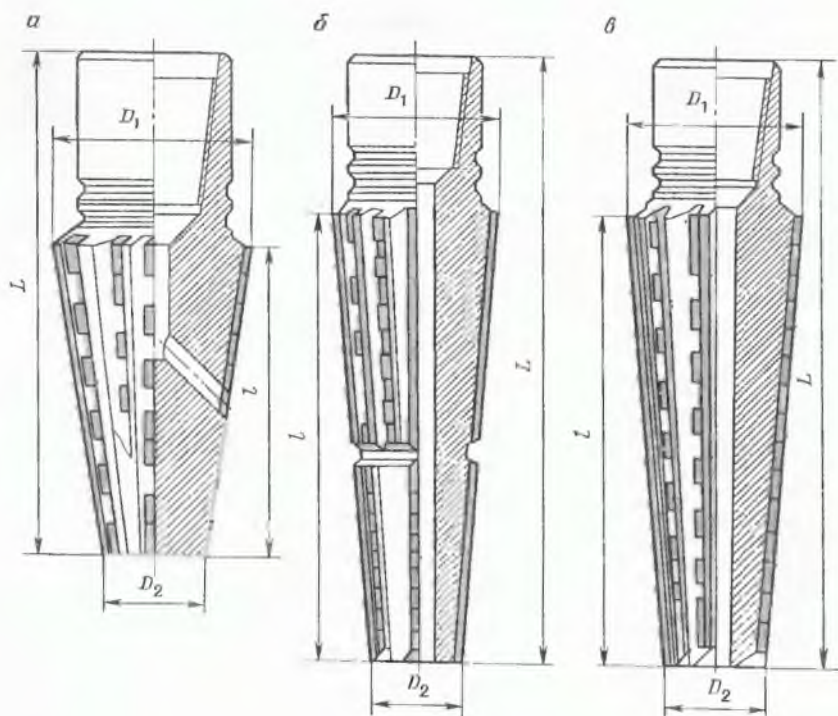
Фрезер-райбер ФРС № 1 (а), № 2 (б) и № 3 (в)
